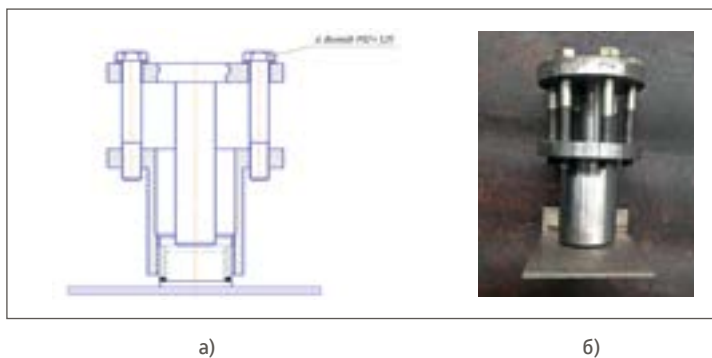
Приспособление для проверки прочности ремонтного фланца подвода топлива:
